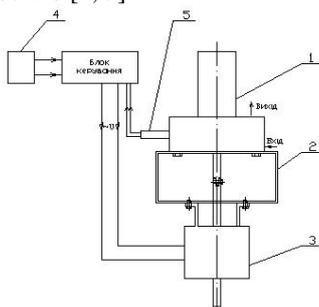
Конструкция блока управления подачей топлива в цилиндр с пьезоприводом: 1 – блок управления подачей топлива; 2 – основа; 3 – пьезопривод; 4 – датчик положения коленчатого вала; 5 – датчик количества впрыснутого топлива
